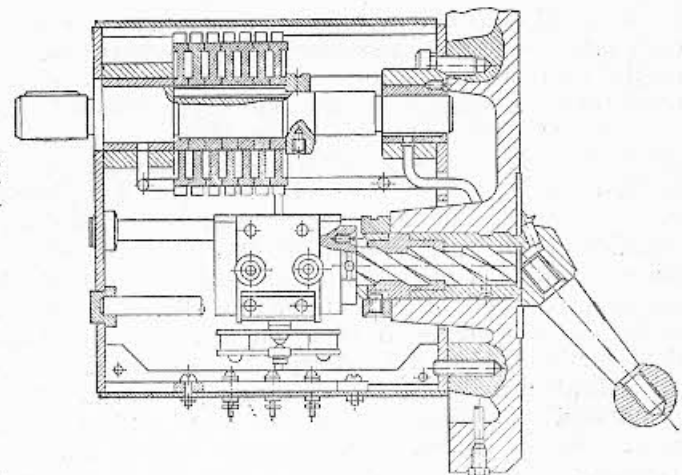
Schema de montaj al mecanismului electric de avans.
